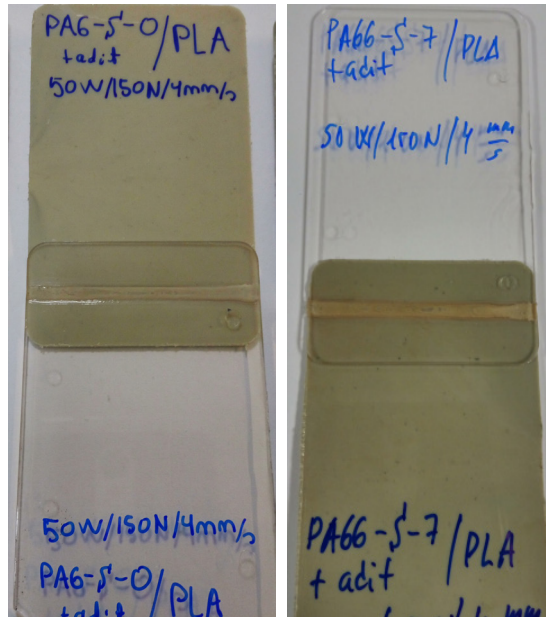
Resultado de la soldadura láser definitiva. A la izquierda, soldadura entre PLA y PA6-S-0+A; a la derecha, soldadura entre PLA y PA66-S-7+A.
